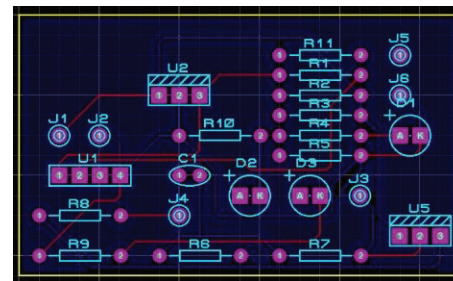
Esquema de la PCB del circuito general Fuente: Propia
